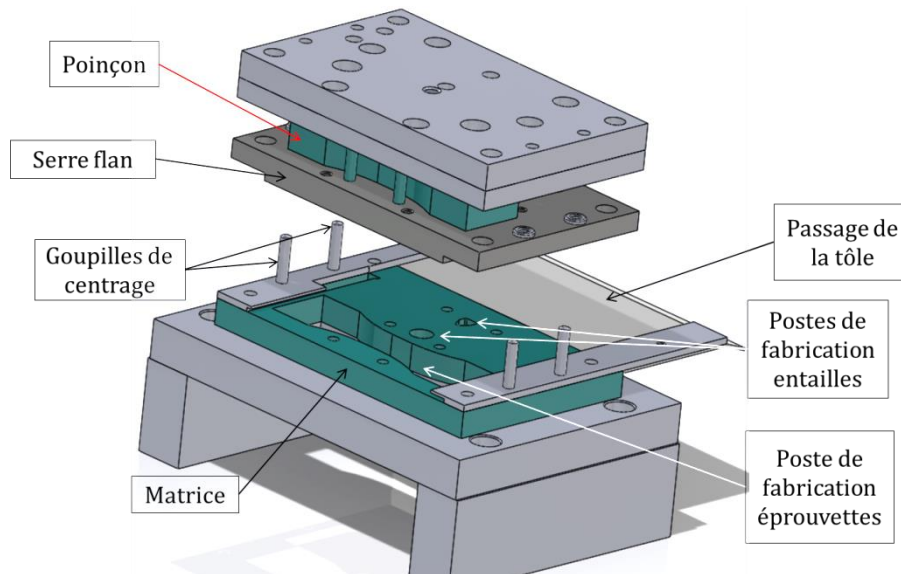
Outil utilisé pour la fabrication des éprouvettes de fatigue lisses et entaillées
